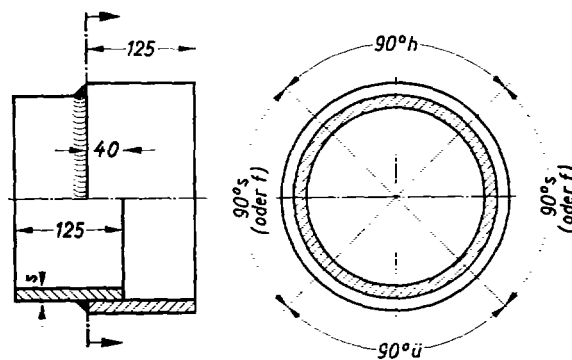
Prüfstück mit Kehlnaht am Überlappstoß für Rohrschweißer an $s \geq 4$ mm
